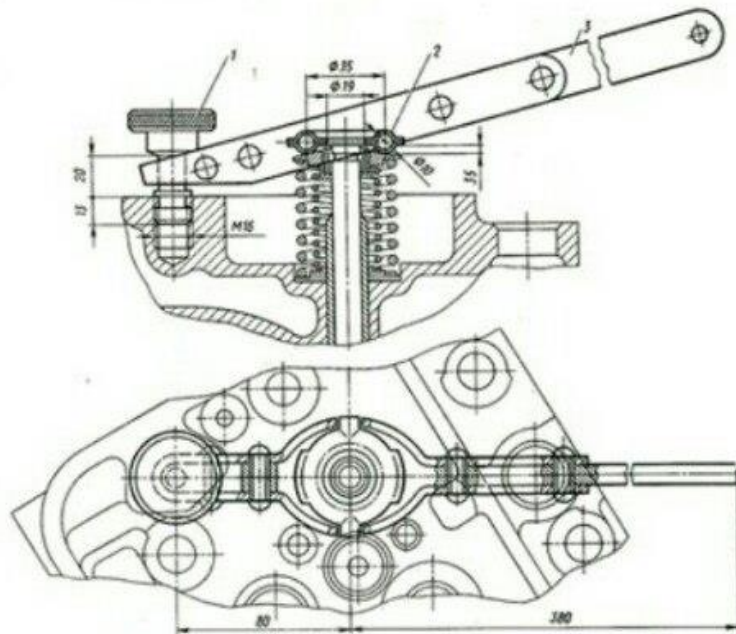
Пристосування для установки клапанів: 1 - упорний гвинт; 2 - нажимна тарілка; 3 – рукоятка
